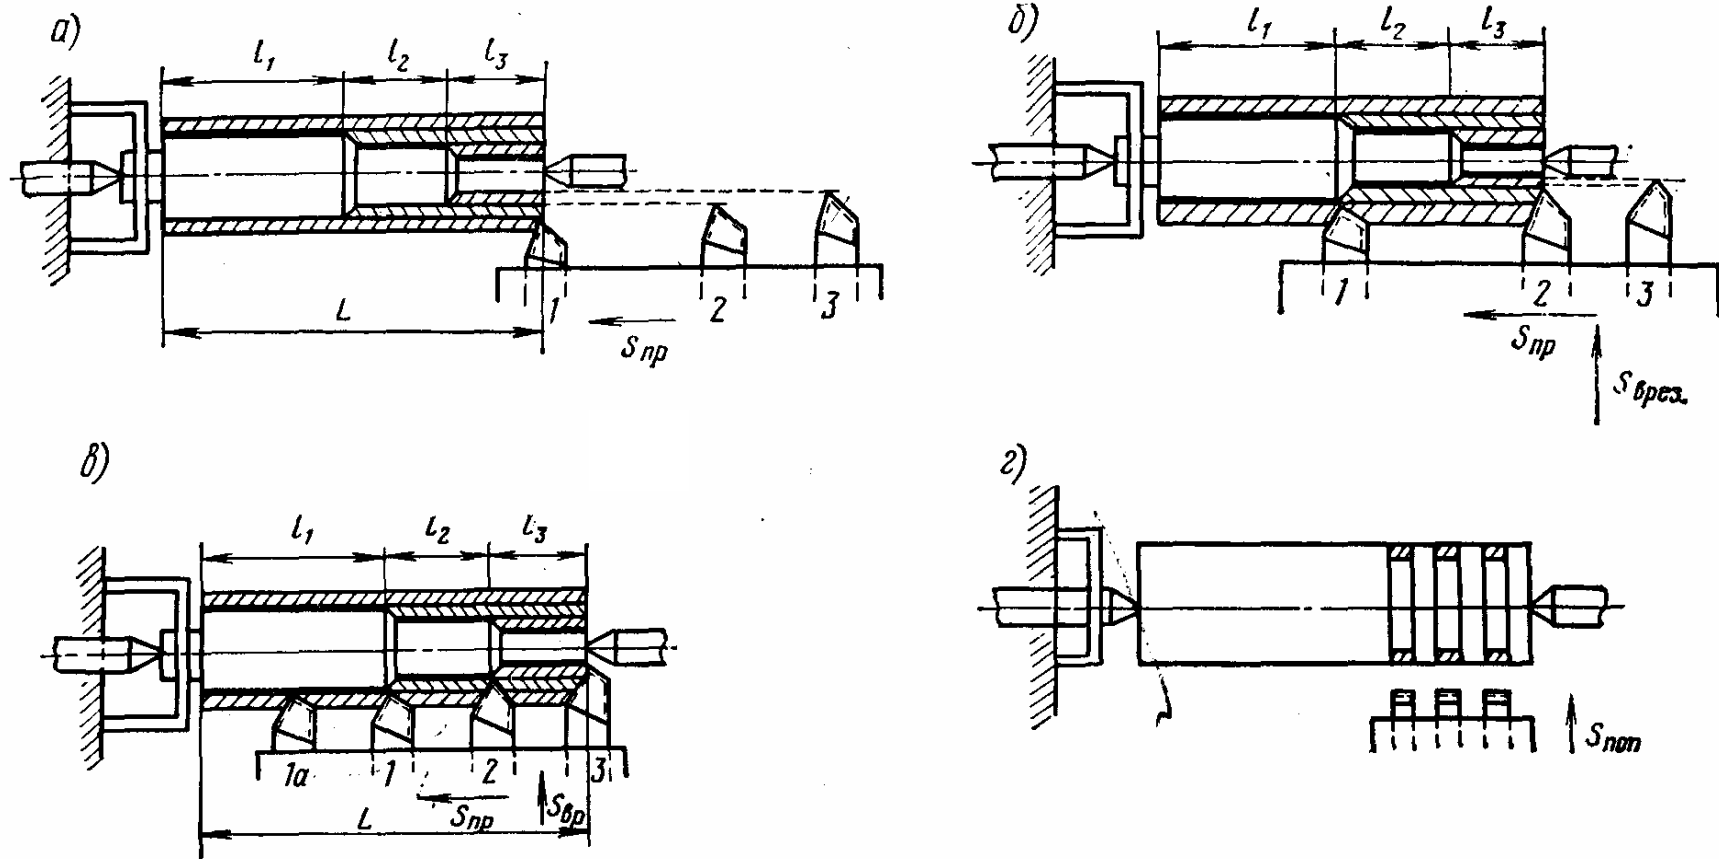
Три способа обтачивания вала на многолезцовом станке
